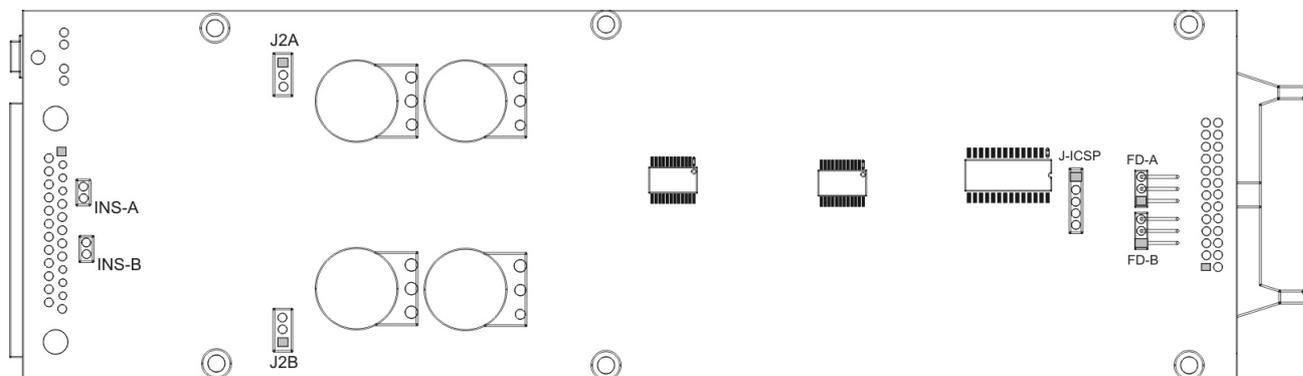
Módulo de micrófono 2610 (vista lado soldaduras)
